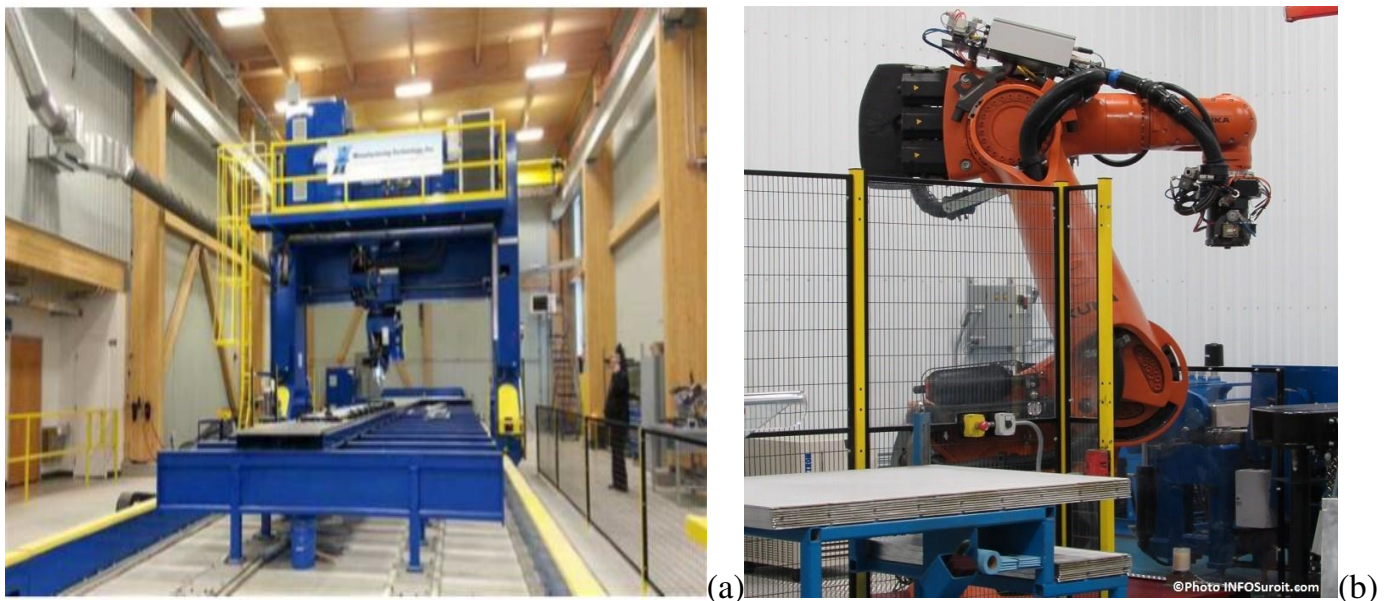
(a) Équipement de soudage conçu pour le FSW [21], (b) Robot doté d'une tête de soudage pour le FSW. [22]
